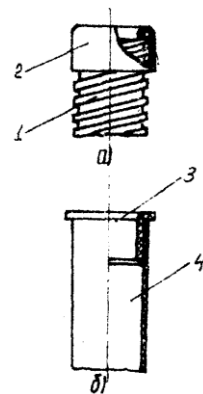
Установка оконцевателей на металлорукава и трубки ПХВ:
